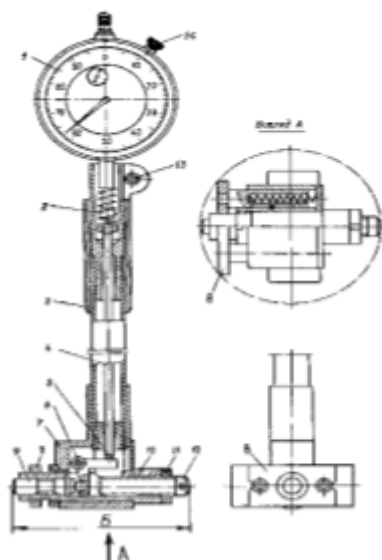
Індикаторний нутромір: 1 – індикаторна головка; 2 – вимірювальний стрижень індикатора; 3 – трубка корпуса; 4 – проміжний вимірювальний стрижень; 5 – двоплечий Г-подібний важіль; 6 – вісь двоплечого важеля; 7 – корпус; 8 – центрувальний місток; 9 – рухомий вимірювальний стрижень; 10 – трійник; 11 – контргайка; 12 – переставний вимірювальний стрижень; 13 – затискний гвинт індикатора; 14 – стопорний гвинт обичайки
